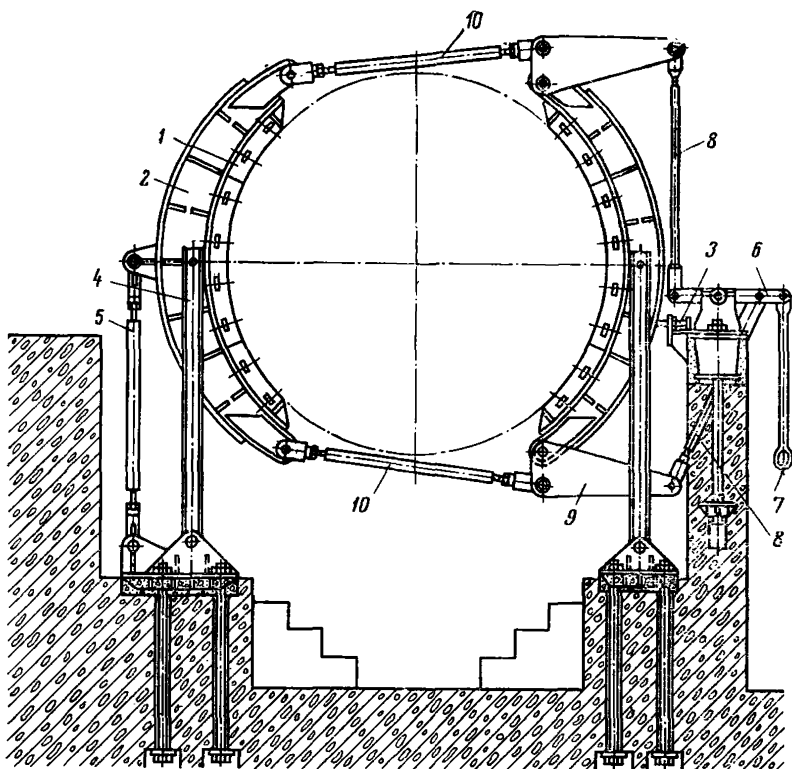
Исполнительный орган тормоза с параллельным перемещением колодок и задним расположением регулировочной стойки:
